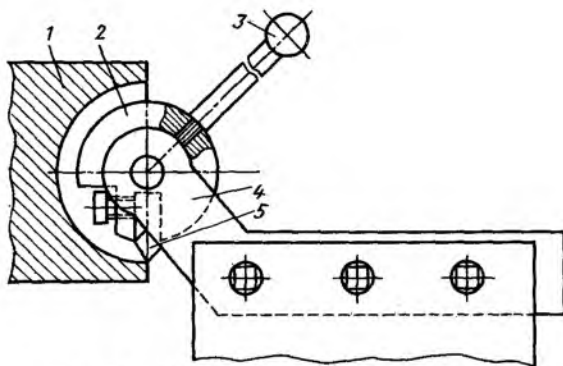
Приспособление для растачивания сферических поверхностей
